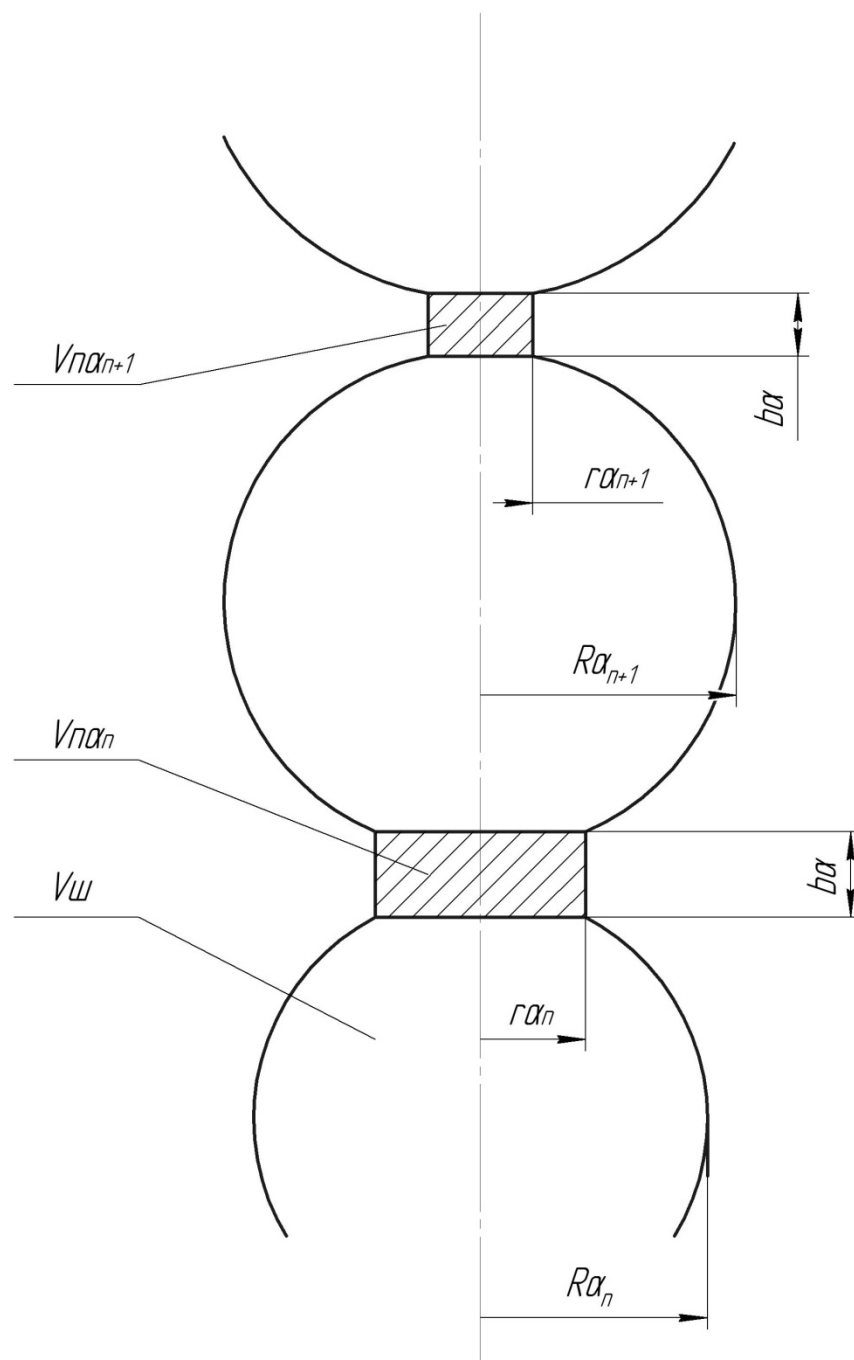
Сечение заготовки во время прокатки с углублением впадины
